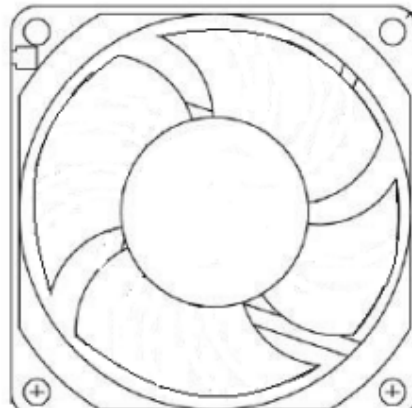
Intercambiador de Calor, Fuente: (Diseño Propio)
